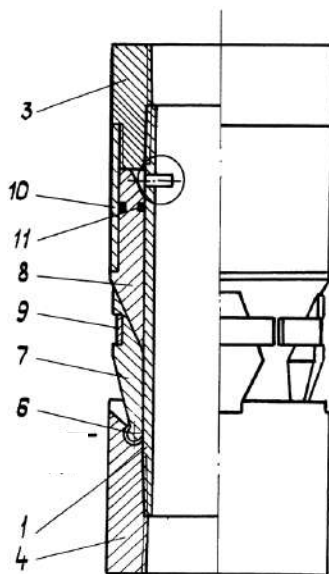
Центратор гидравлический [2]: 1 – обсадная труба; 2 – отверстия; 3, 4 – муфты; 5 – кольцевая канавка; 6 – оси; 7 – рычаги; 8 – рабочий поршень; 9 – разрезное пружинное кольцо; 10 – цилиндр; 11 – резиновые кольца
